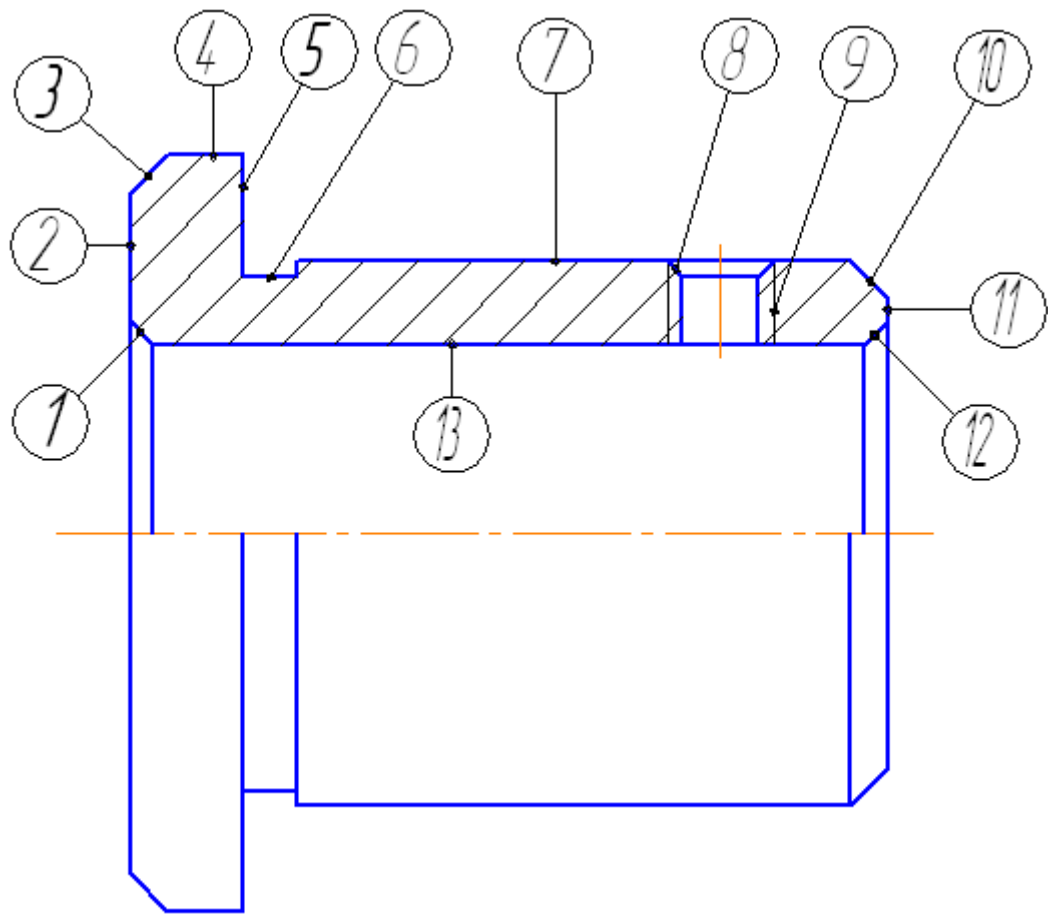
Ескіз деталі із номерами її поверхонь
